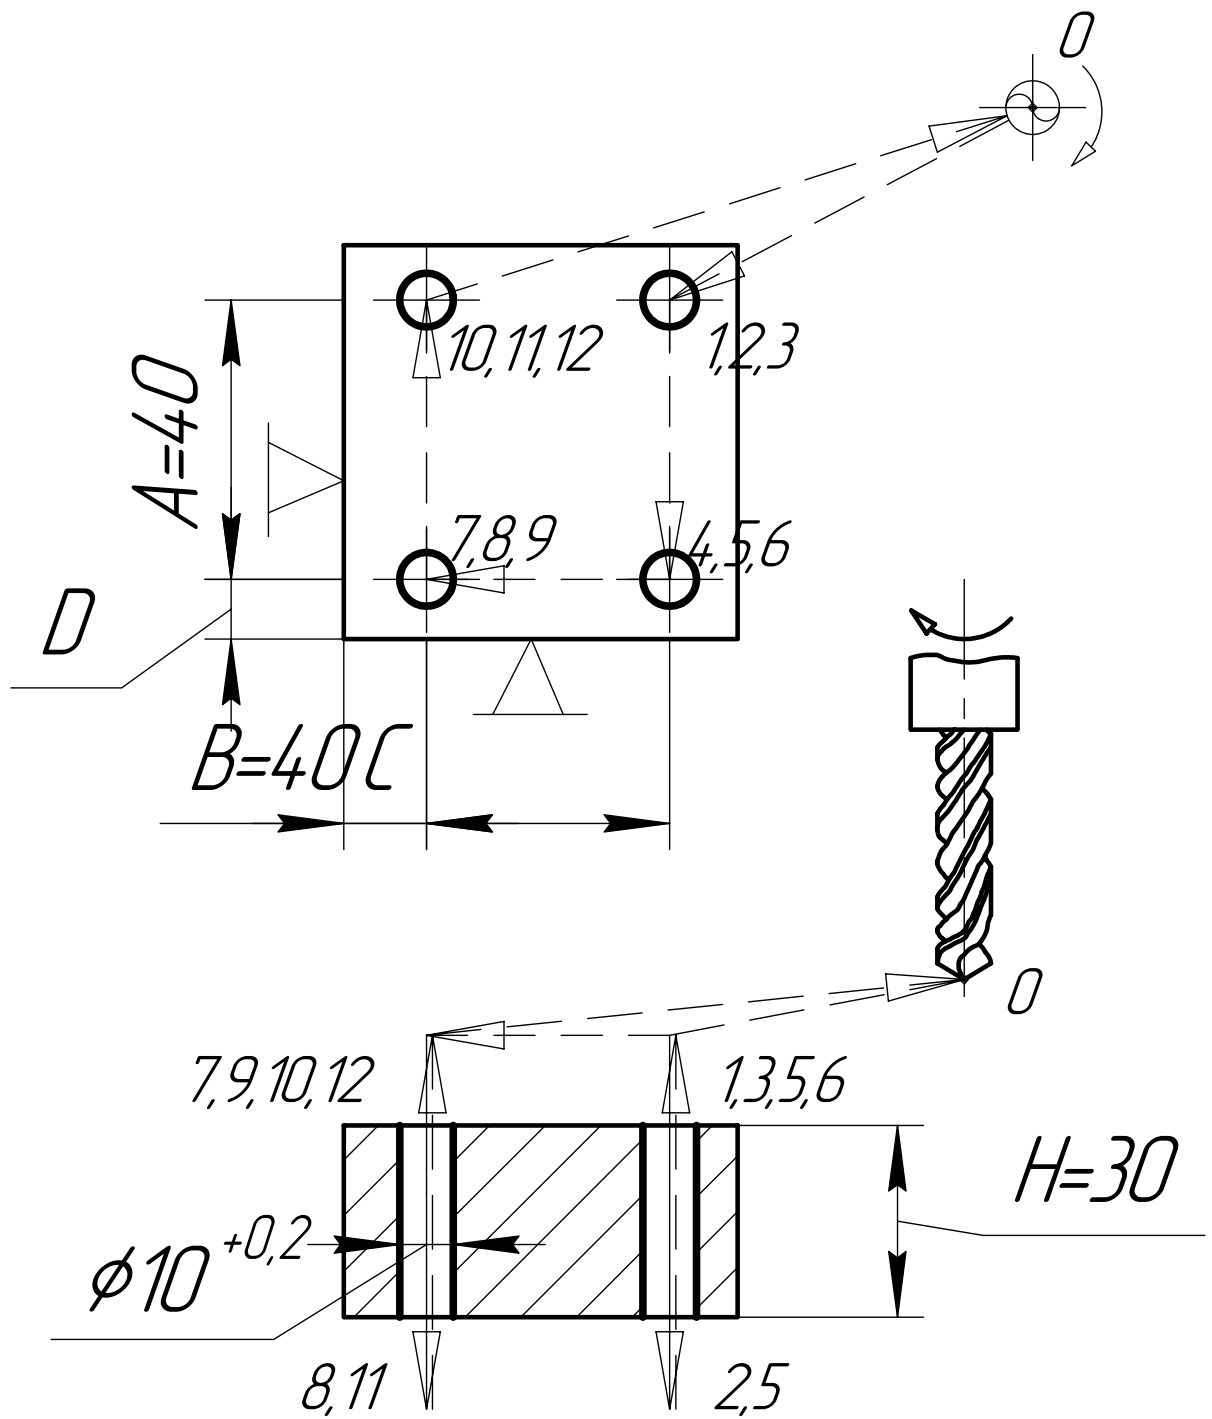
Сверление 4-х отверстий на станке с ЧПУ
